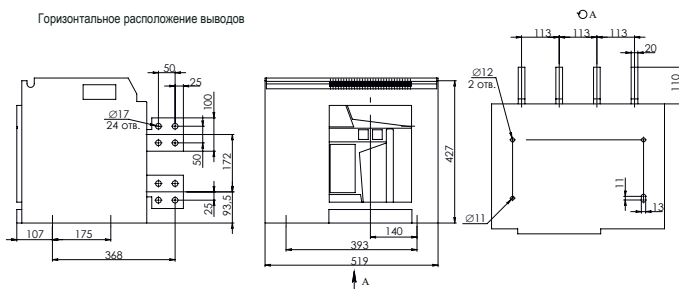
Габаритные размеры выдвижных трехполюсных выключателей типоразмера E In = 2500, 3200 A
